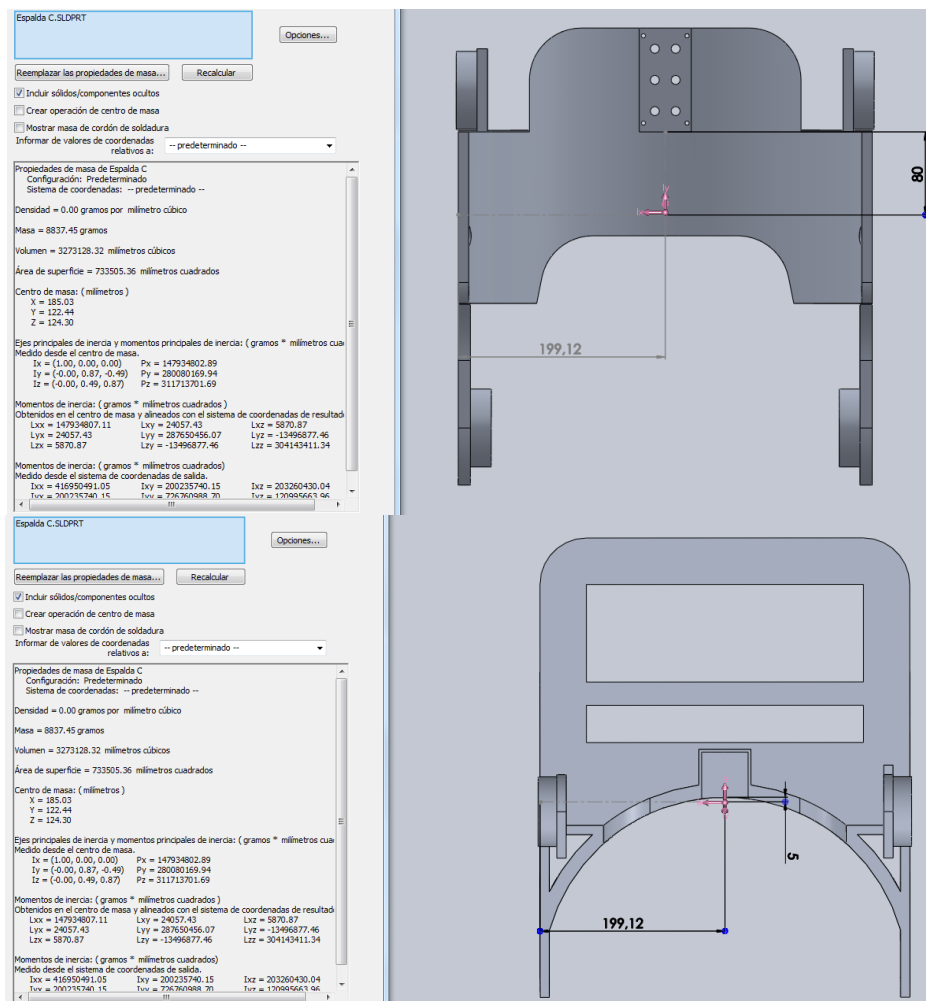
Centro de masa del ensamblaje de sección C - espalda
